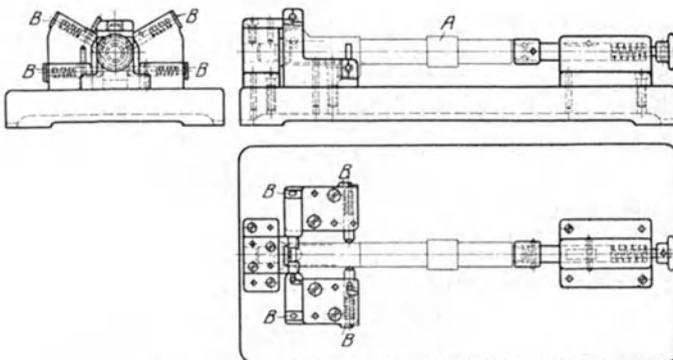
Vierfache Revisionseinrichtung mit Fühlstiften.
